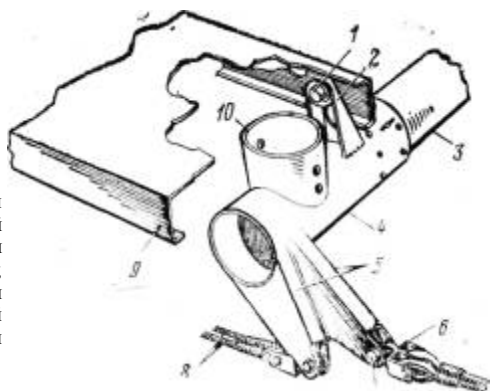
2. Поперечная труба с узлами и ее подвеска к силовой балке:
